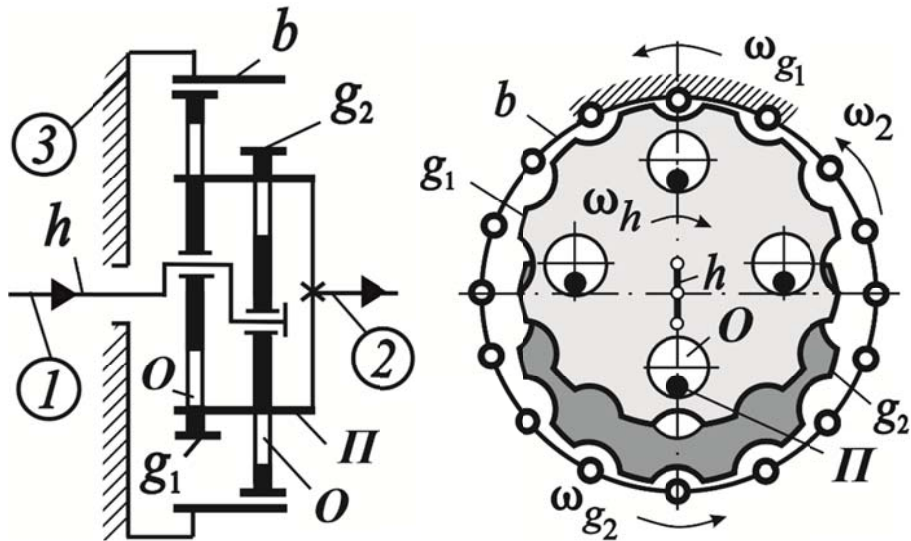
Схема планетарно-кривошипного механизма цевочного эпициклоидального зацепления с двумя оппозитными сателлитами (звездочками)
